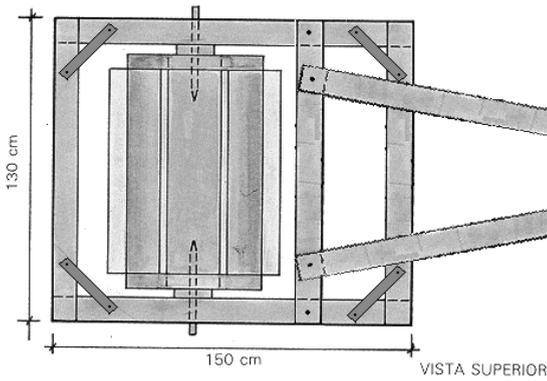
A moldura tem que ser montada introduzindo-se os dois
